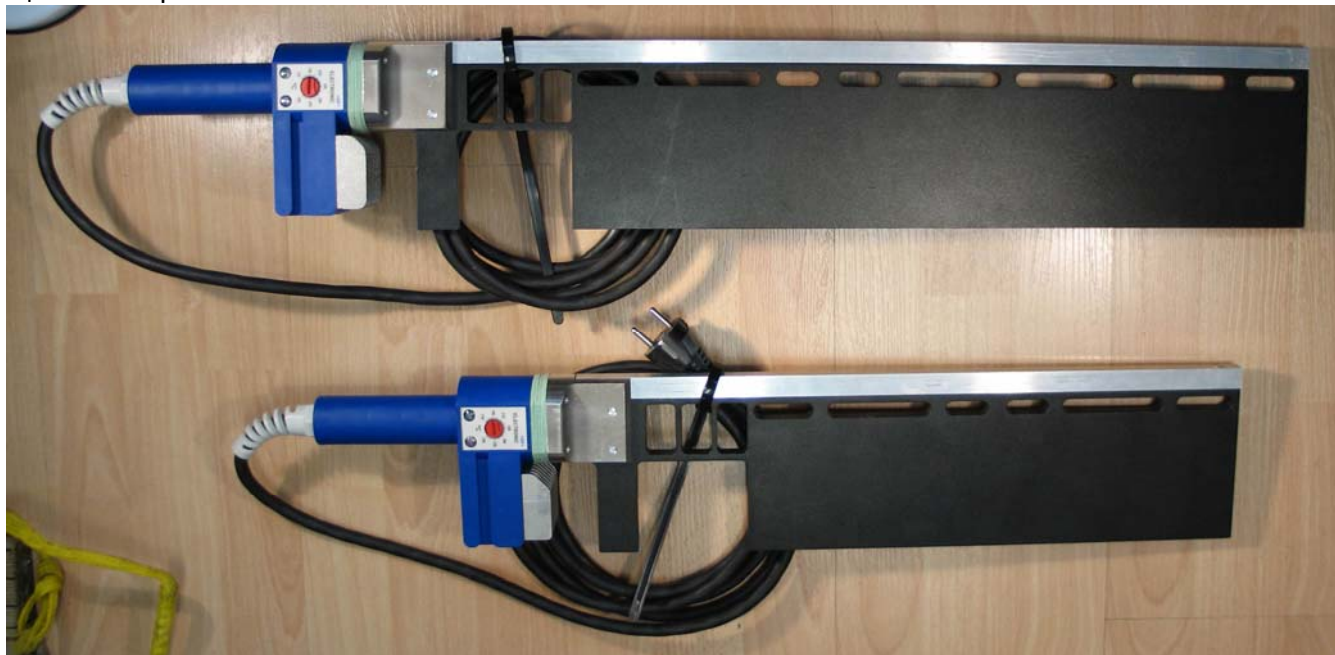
Аппараты для стыковой сварки моделей Л-500 (сверху) и Л-340 (снизу).
